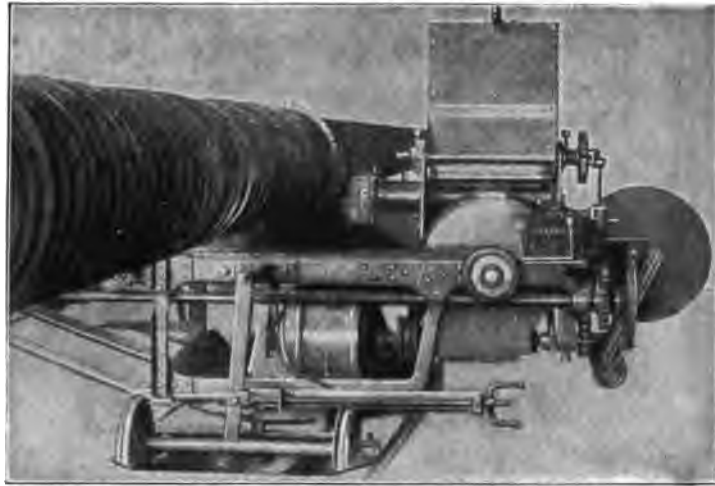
Maschine zur Herstellung von hohlen Eisenbetonmasten (Siegwartmasten) mit Kernform und teilweise aufgetragener Betonschicht.¹⁾
